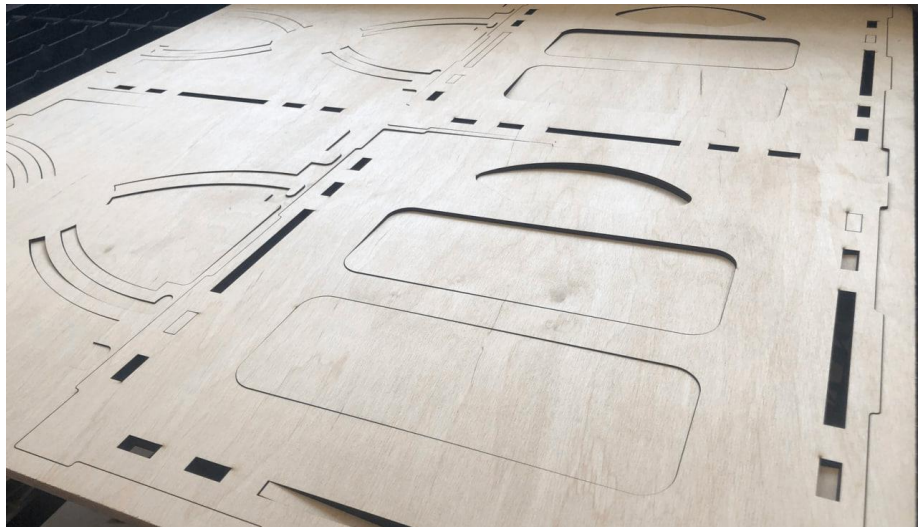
виготовлення деталей на фанерному листі за допомогою лазерного верстата
